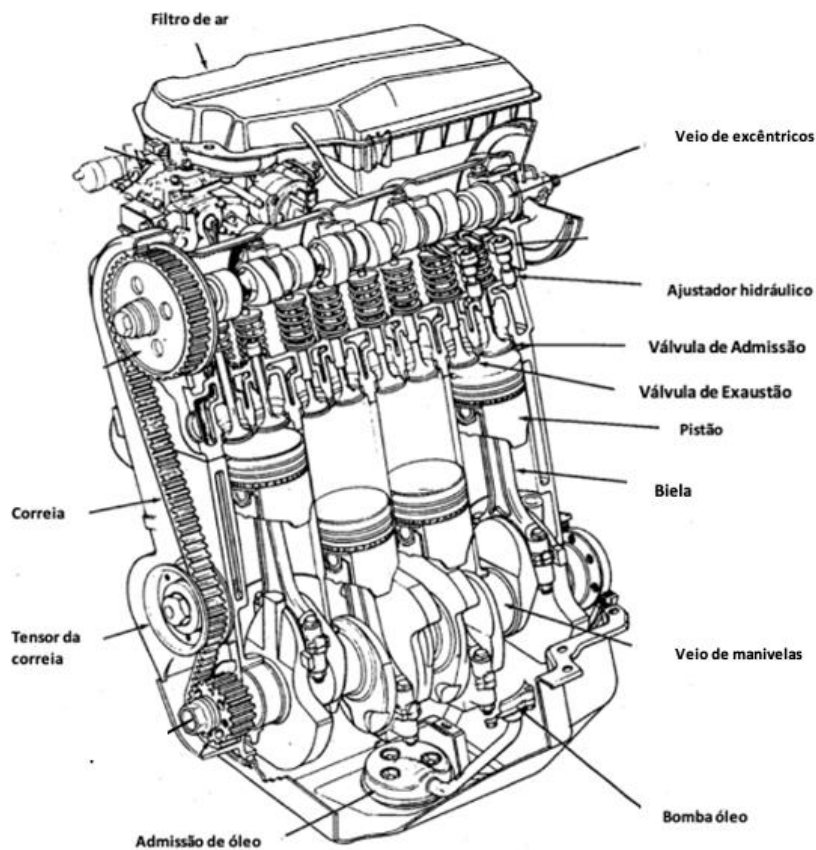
Constituição de um motor de combustão interna (adaptado [8]).
